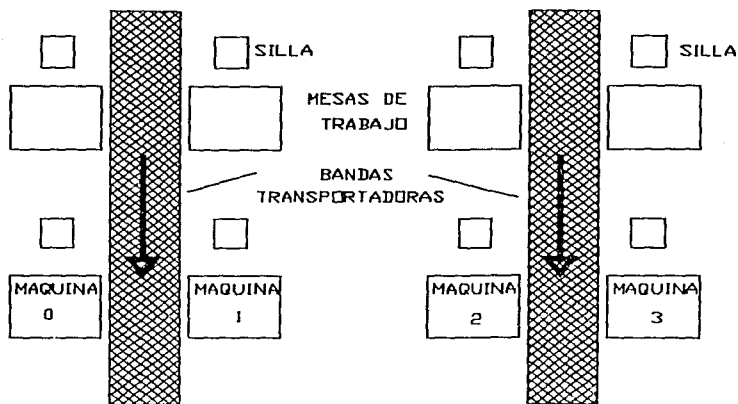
Vista de planta de las máquinas soldadoras
